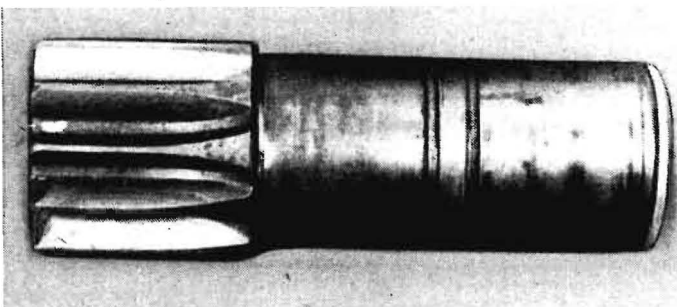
Instandsetzungsschweißung durch Reibschweißen
